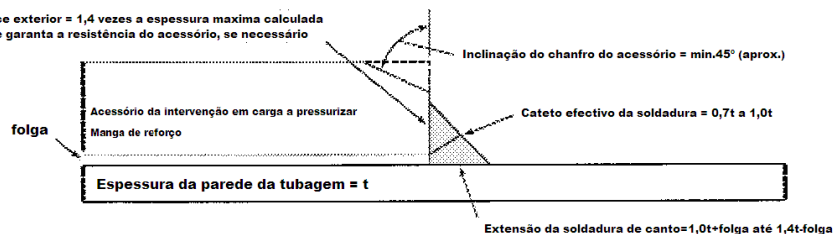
Dimensionamento da geometria do cordão de soldadura e posicionamento de cordões
